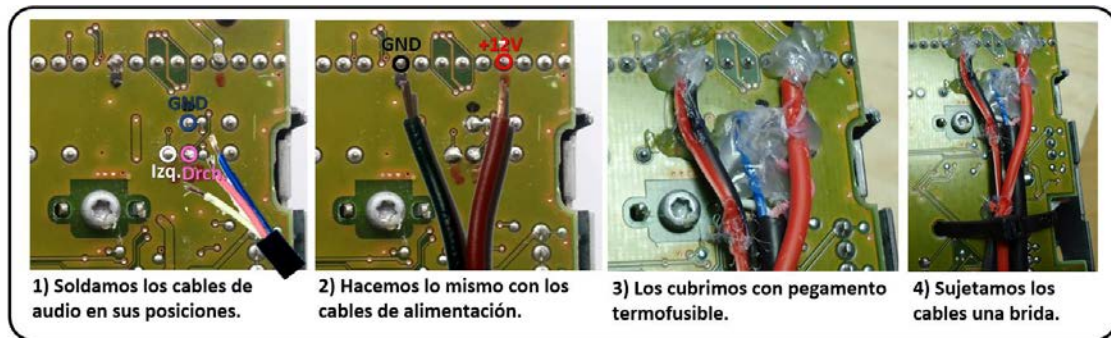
Soldadura de los cables a la placa (Nº Fig. 166).
